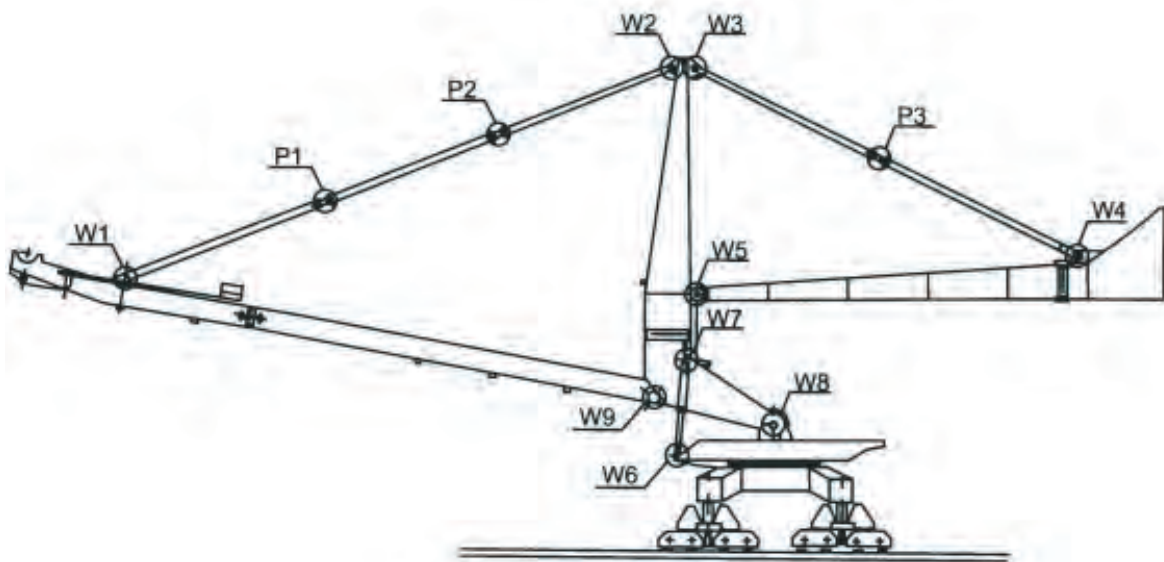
Konstrukcja nośna koparki SchRs 4000 w KWB Belchatów
